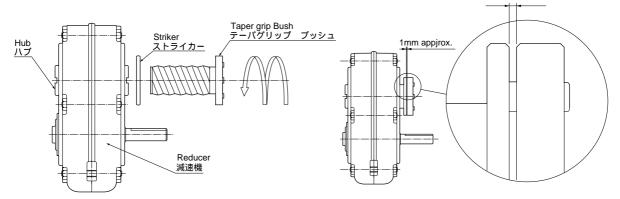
ブッシュを減速機にとりつける Figure 1. Bush Attachment to the Reducer
